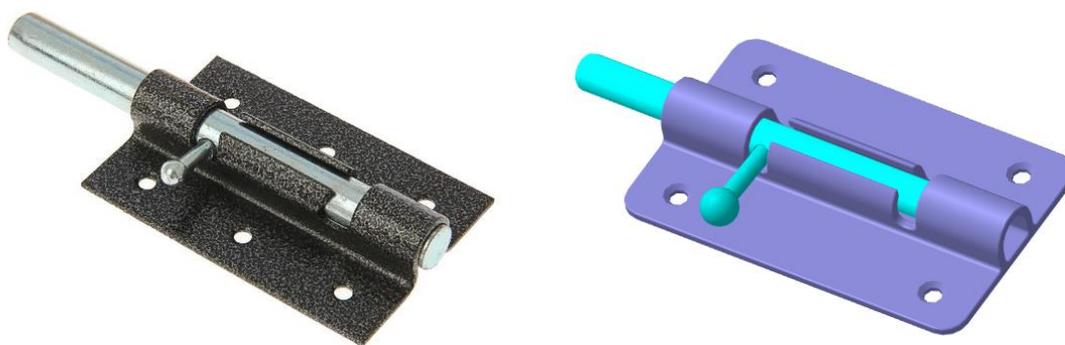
Образец и модель изделия «Задвижка дверная (шпингалет)»
